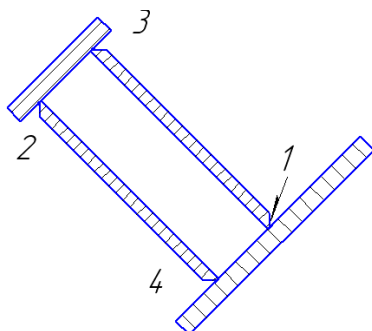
Положение заготовки при сварки шва №1
